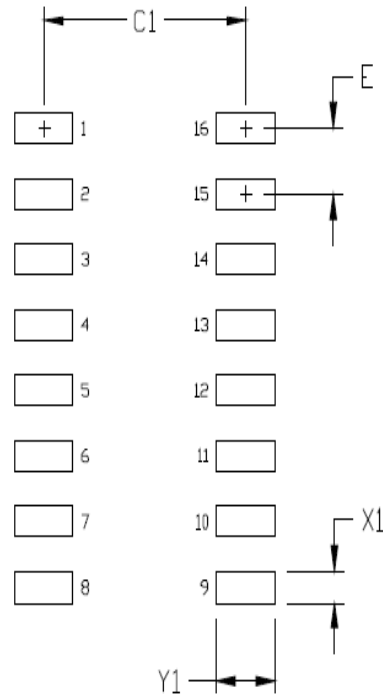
16 引脚窄体 SOIC PCB 焊盘图案
